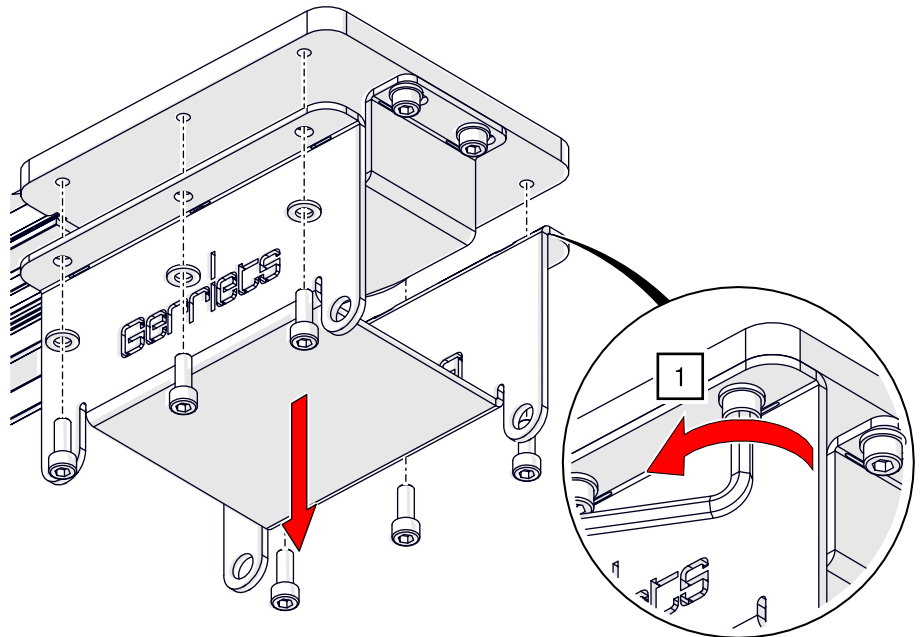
Zahnriemenmontage – Gehäuse der Umlenkungen öffnen
